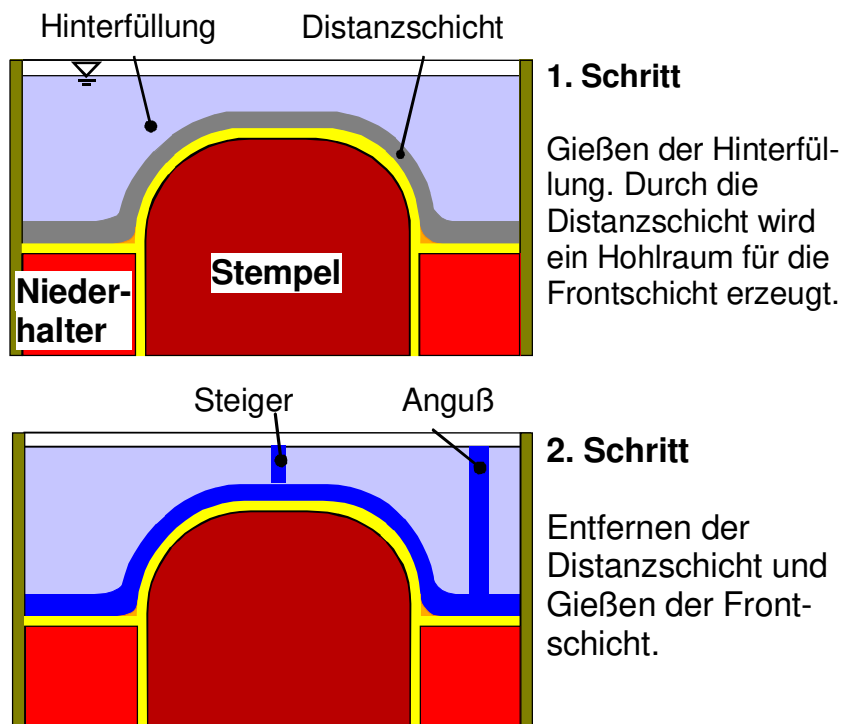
Herstellung von Tiefziehwerkzeugen im Frontgußverfahren
